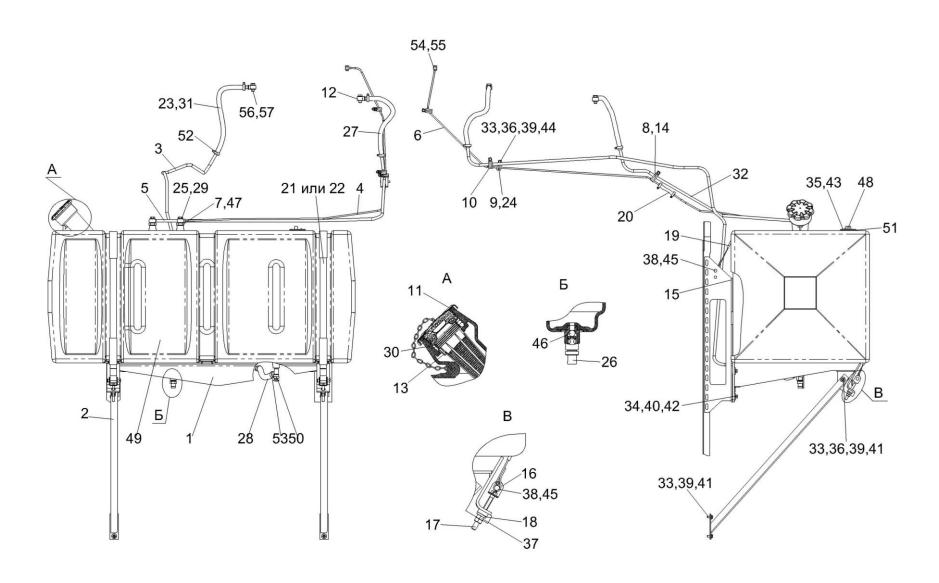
Установка бака топливного КЗК-8А-0126000
